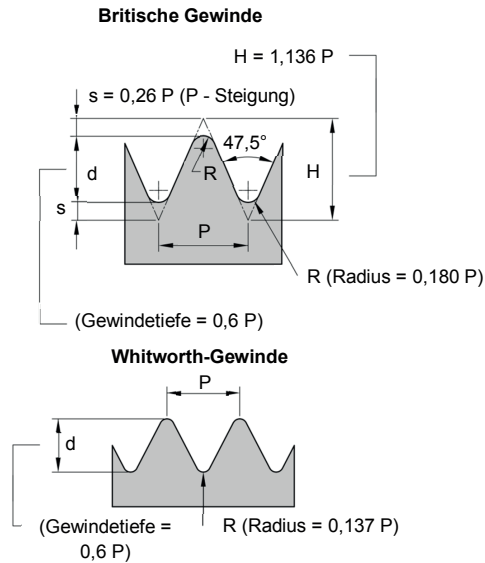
Geeignete Gewindegeometrie für Spritzgussteile
